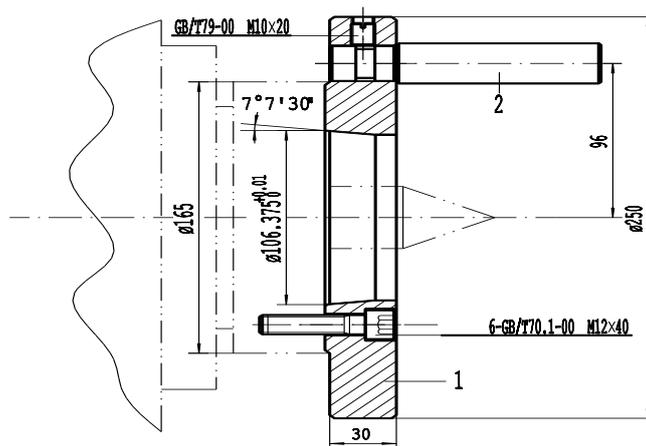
Схема установки патрона, установочной плиты или планшайбы
